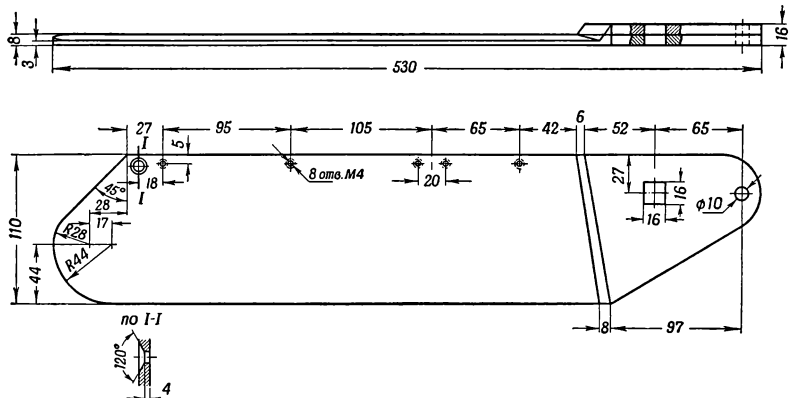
а. Чертеж и размеры метательной платформы к машинкам образца Б. Крейцера и В. Щербакова
